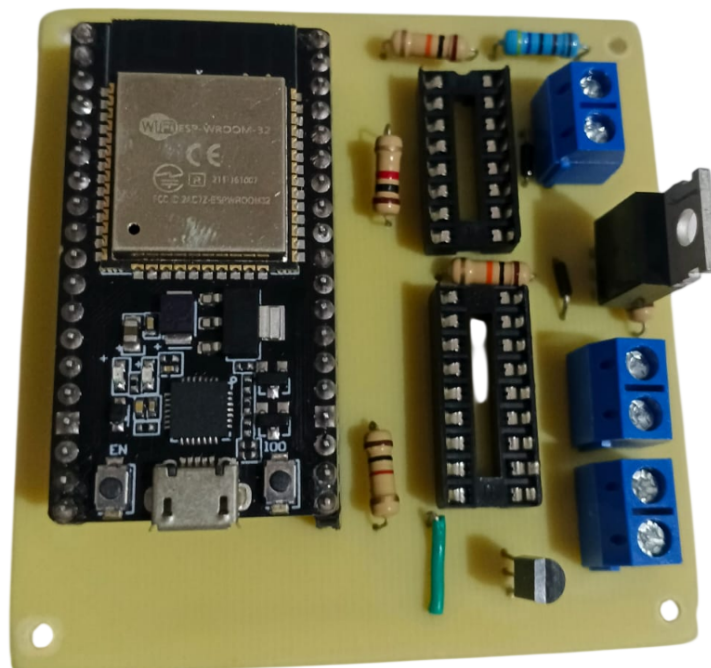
Prototipo de placa PCB: montaje de componentes. Autor Propio
